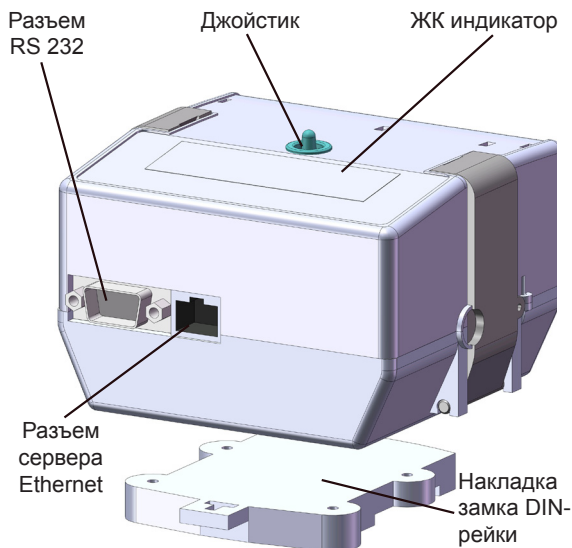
б - Вид на корпус СТУ-1 сзади
